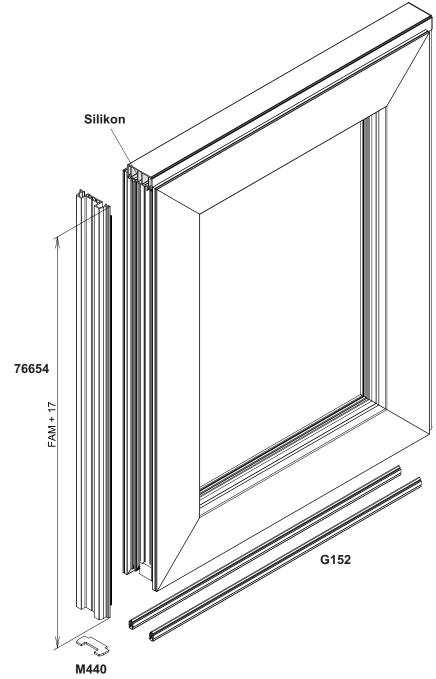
Zuschnitt und Bearbeitung Einlaufprofil 76654
